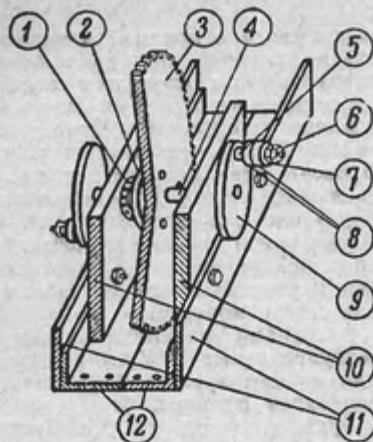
Узел кулисы в сборе: 1 — шариковые подшипники 30×10 мм (2 шт.); 2 — фланец оси; 3 — ведомая шестерня; 4 — ось кулисы; 5 — ось щетки; 6 — гайка с контргайкой; 7 — кулачок кулисы; 8 — шариковые подшипники 22×8 мм (2 шт.); 9 — щетка кулисы; 10 — стойки кулисы; 11 — накладки; 12 — угловой дюралюминий (30×30 мм).
